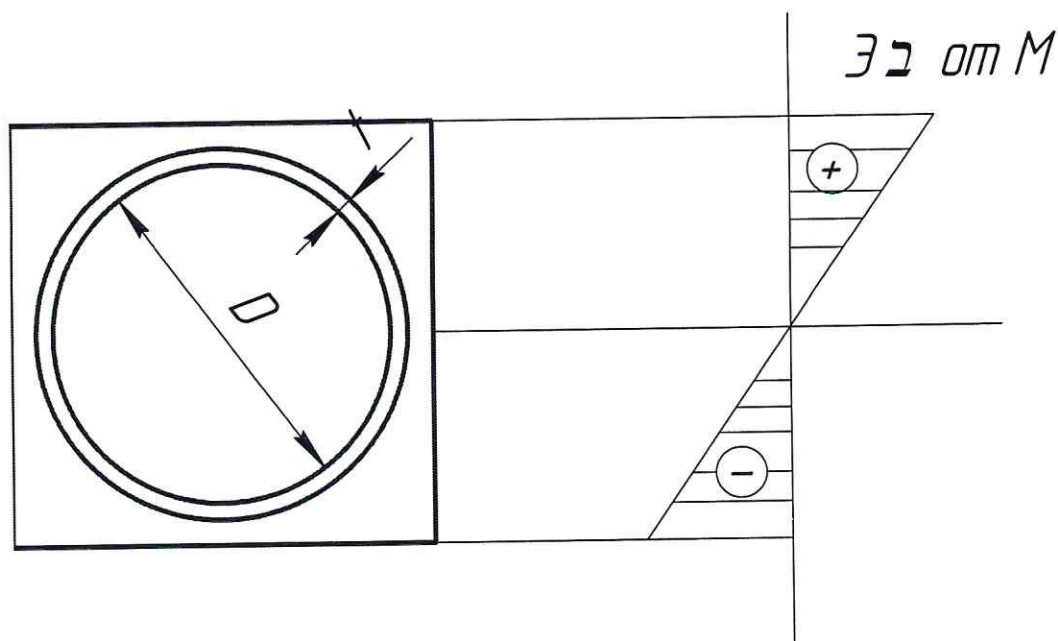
Эпюра изгибающего момента в месте сварного шва
